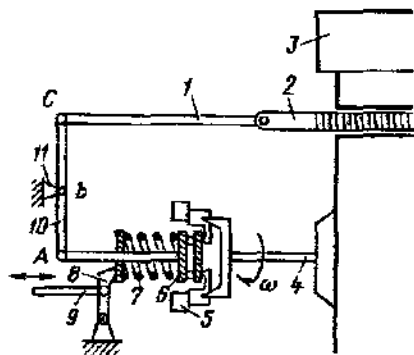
Принципиальная схема регулятора скорости прямого действия: 1 - тяга, воздействующая на топливную рейку; 2 - топливная рейка; 3 - двигатель; 4 - приводной вал; 5 - центробежные грузы; 6 - муфта; 7 - задающая пружина; 8 и 9 - соответственно рычаг и тлга, изменяющие затяжку пружины задания; 10 - рычаг; Л - опора рычага
